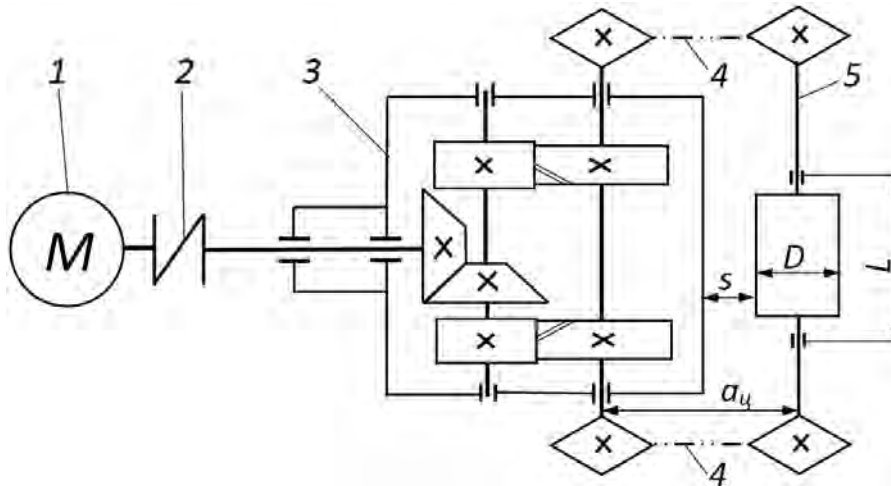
Схема привода ленточного транспортера (вид сверху): 1 – асинхронный электродвигатель; 2 – муфта упругая с резиновой звездочкой; 3 – редуктор коническо-цилиндрический (расположение конической шестерни с круговым зубом симметрично относительно стенок корпуса редуктора, вторая ступень с двумя косозубыми цилиндрическими зубчатыми передачами с разделенным потоком мощности); 4 – цепные передачи; 5 – приводной вал с барабаном
